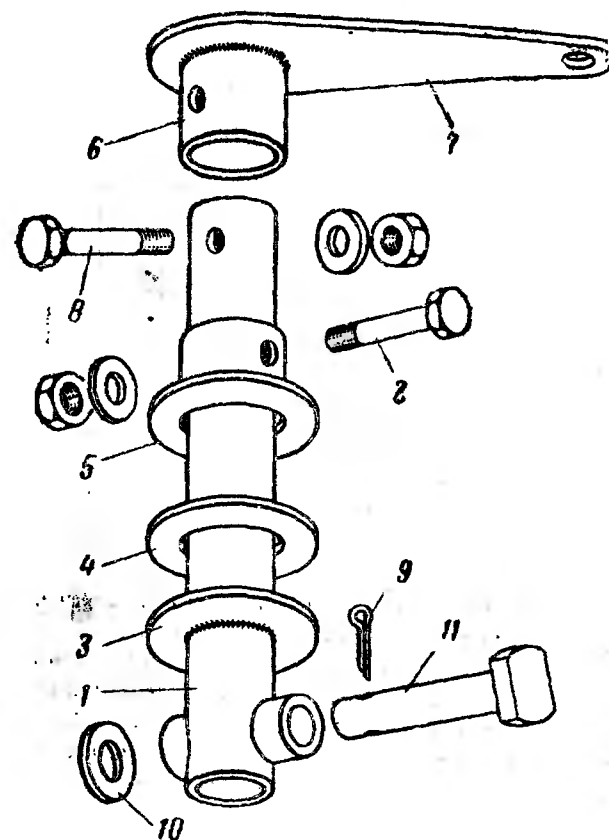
Колонка передней управляемой лыжи аэросаней простейшего типа: 1 — труба передней колонки; 2 — болт; 3 — упорный фланец; 4 — латунная опорная шайба; 5 — верхний упорный фланец; 6 — втулка румпеля; 7 — румпель; 8 — болт крепления румпеля; 9 — шплинт; 10 — шайба, 11 — болт крепления кабанчика лыжи.
